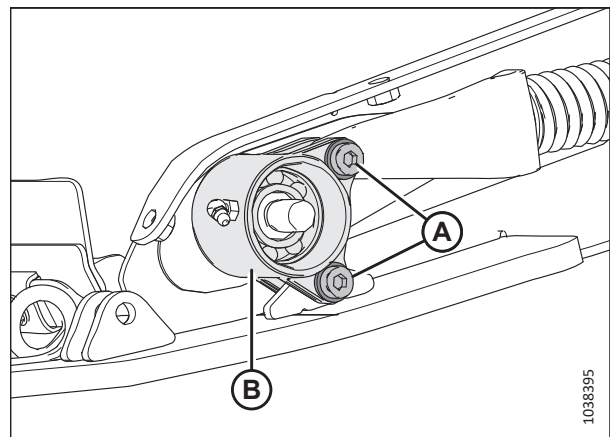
Carcasa del rodamiento del rodillo tensor
